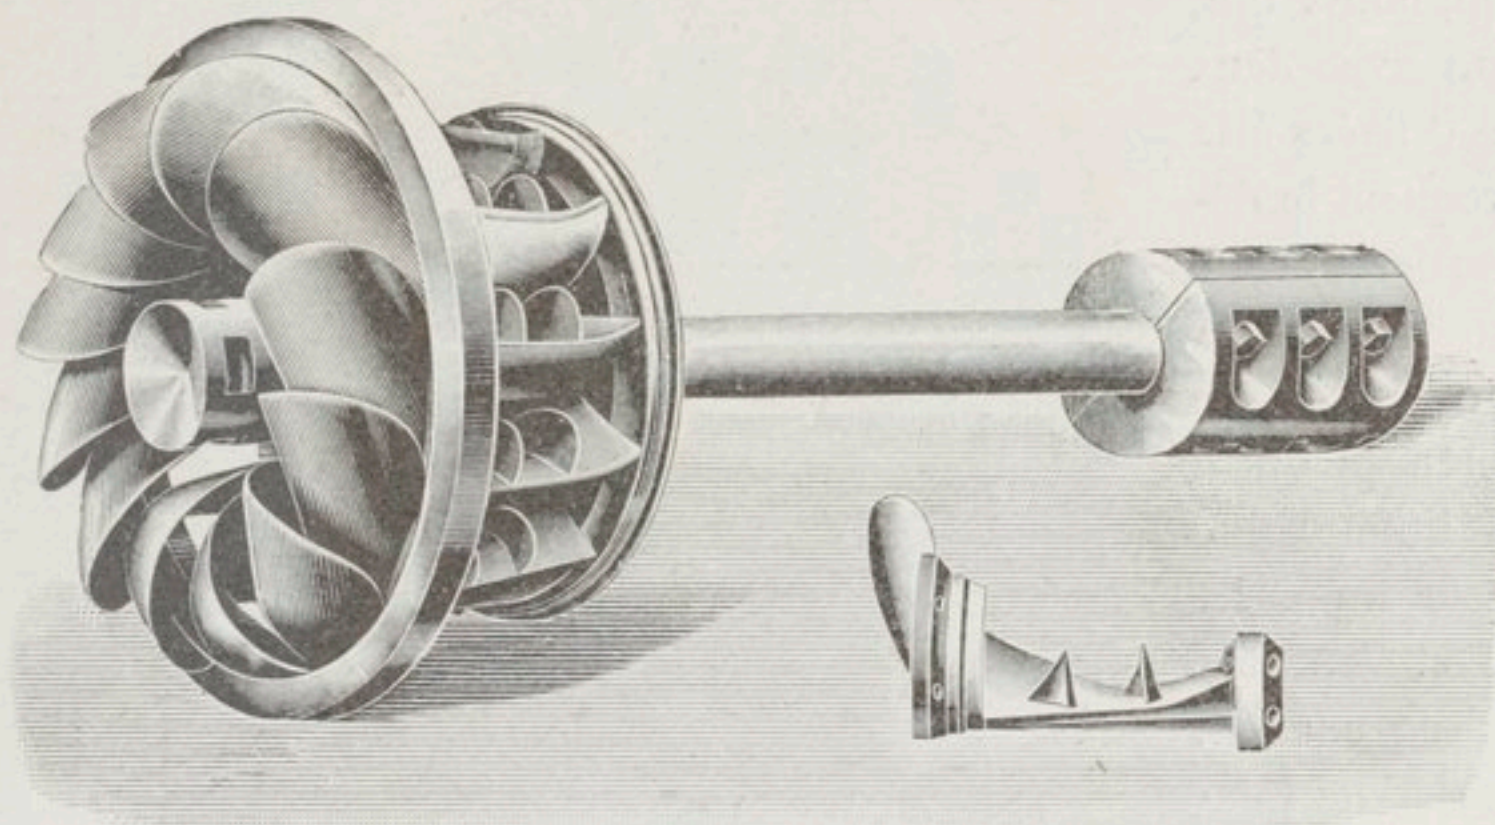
Turbine Hercule-Progrès. — Distributeur assemblé.
